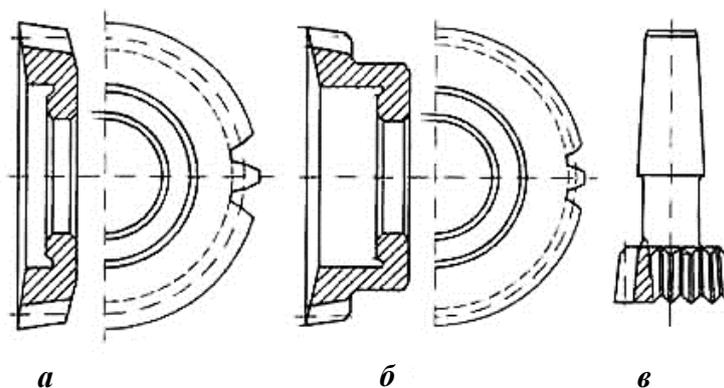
Схемы работы и конструкция зуборезного долбяка
